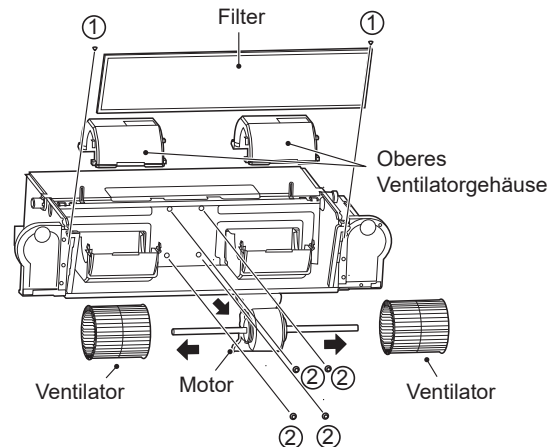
Entfernen des Filters, des Oberteils und der Schrauben des Motors
